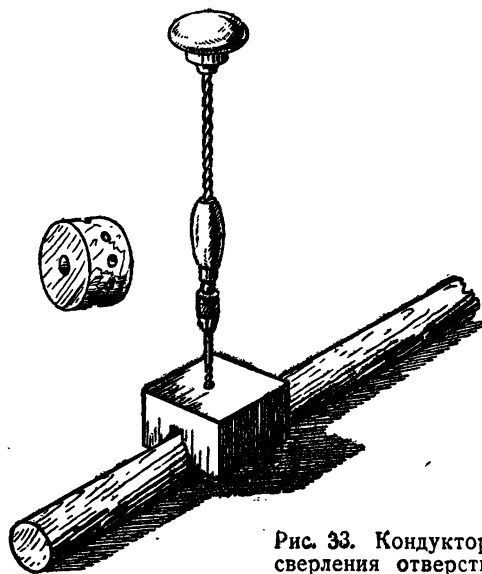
Кондуктор для сверления отверстий по радиусу в цилиндрических деталях.
